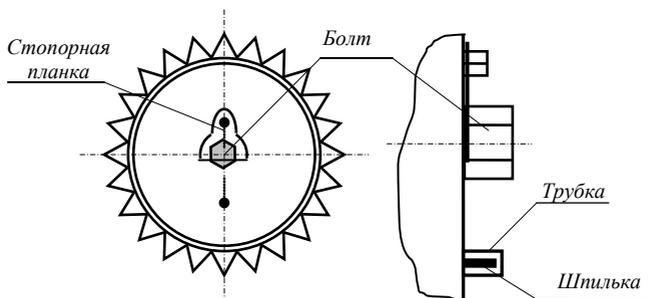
Схема к регулированию предохранительной муфты привода ковшовой цепи
